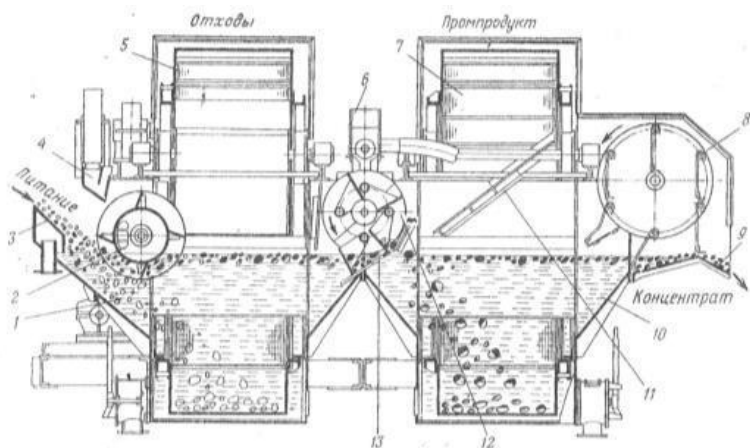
Сепаратор СТТ трехпродуктовый с вертикальными элеваторными колесами:
